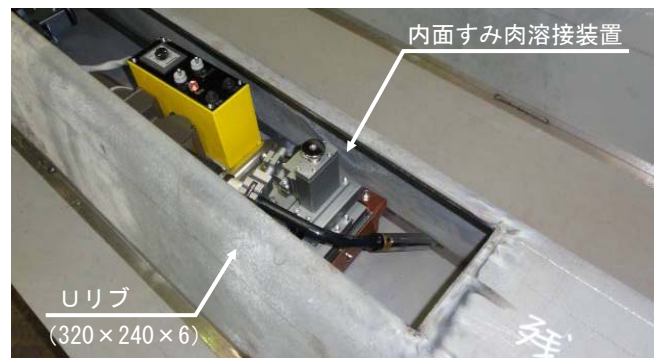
Uリブ内の内面すみ肉溶接装置
